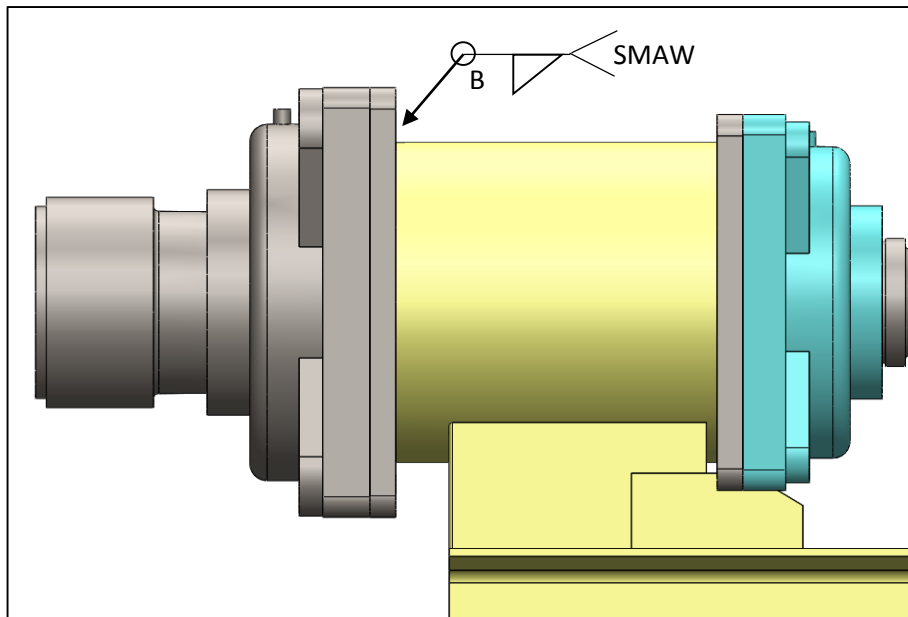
Soldadura entre base para chumacera de pared y tubo.
